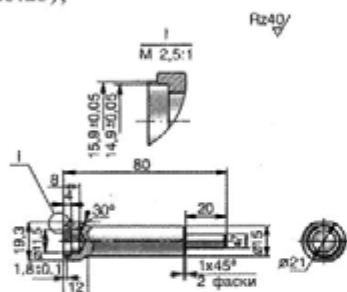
Оправка для сборки гидронатяжителя
